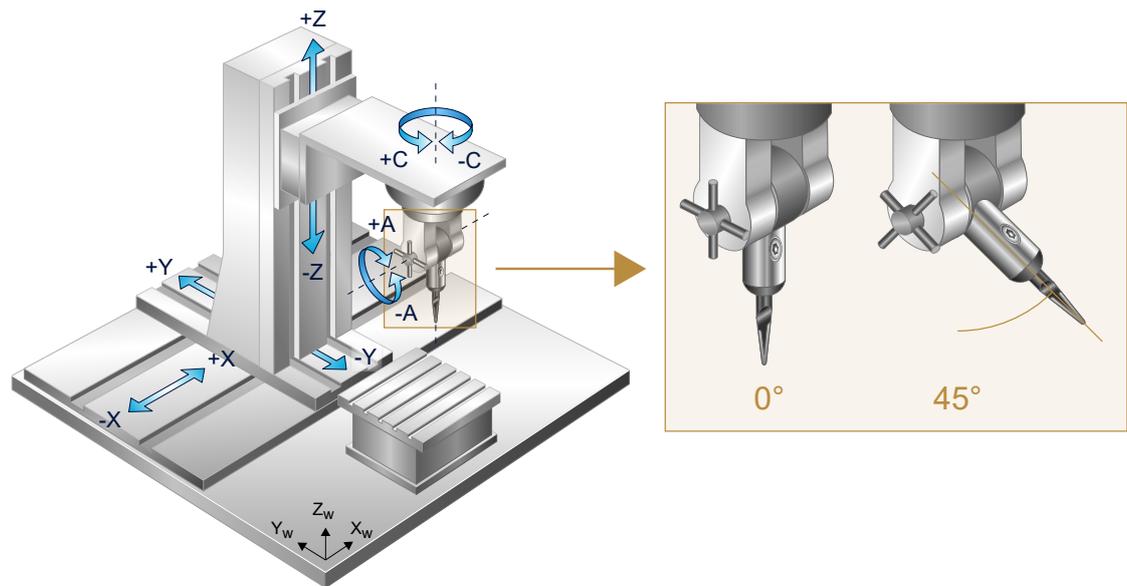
5-achsige Kinematik (Schneidwerkzeug mit manueller Hilfsachse A)
